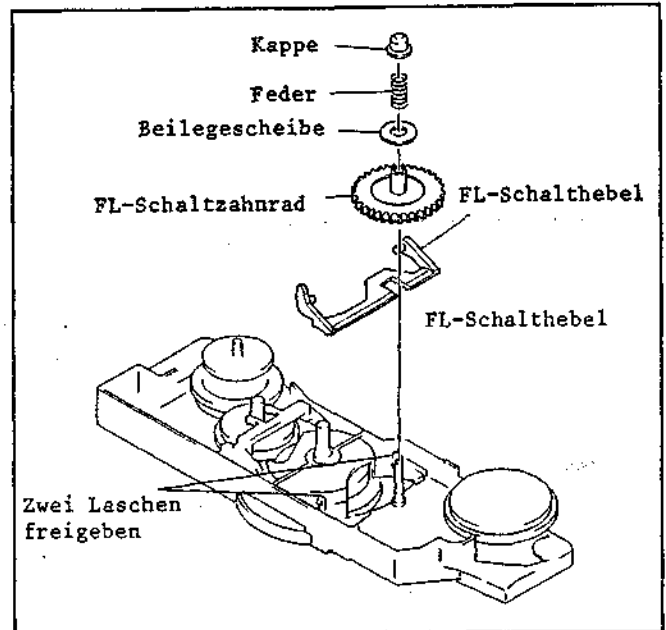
FL-Schaltzahnrad, FL-Schalthebel
